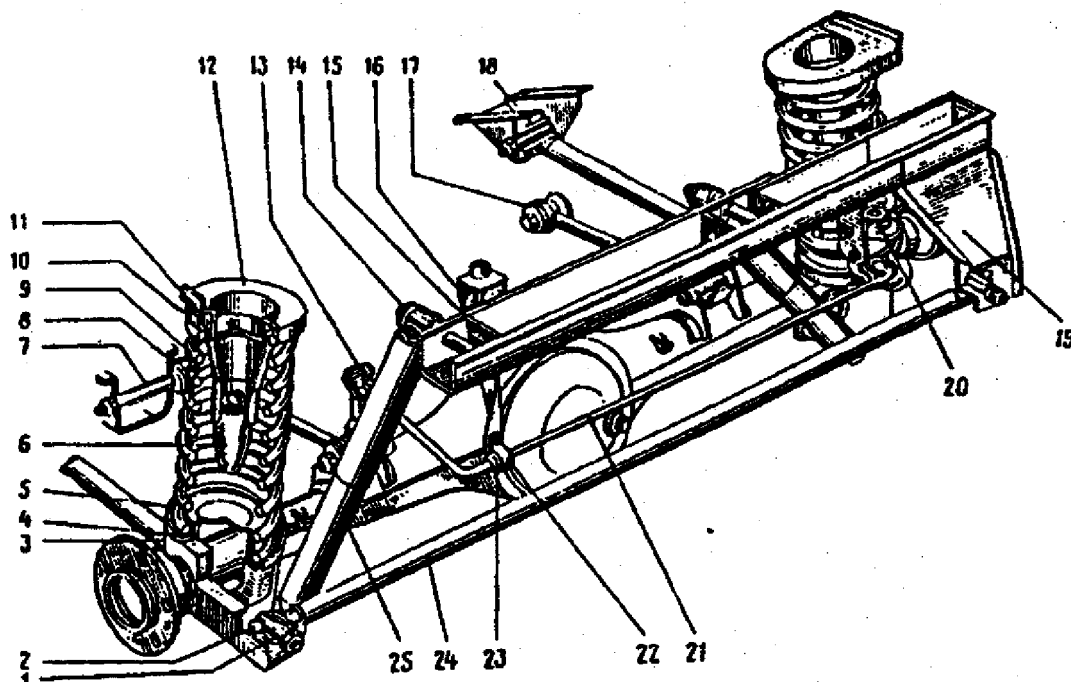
Suspensão traseira: 1 - bucha espaçadora; 2 - coxim; 3 - barra longitudinal inferior; 4 - isolador inferior da mola; 5 - suporte inferior da mola; 6 - batente da suspensão; 7 - parafuso de fixação da barra longitudinal superior; 8 - suporte de fixação da barra longitudinal superior; 9 - mola da suspensão traseira; 10 - suporte superior da mola; 11 - isolador superior da mola; 12 - suporte superior; 13 - haste da alavanca de acionamento do regulador da pressão dos freios traseiros; 14 - isolador do olhal do amortecedor; 15 - travessa do assoalho da carroceria; 16 - batente suplementar da suspensão; 17 - barra longitudinal superior; 18 - suporte de fixação da barra longitudinal inferior; 19 - suporte de fixação da barra transversal à carroceria; 20 - regulador de pressão; 21 - alavanca de acionamento do regulador de pressão; 22 - suporte de articulação da alavanca; 23 - articulação da alavanca; 24 - barra transversal; 25 - amortecedor.
